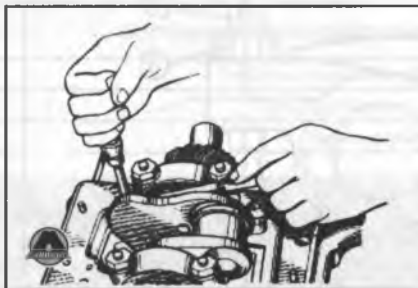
Проверка осевого зазора коленчатого вала.
